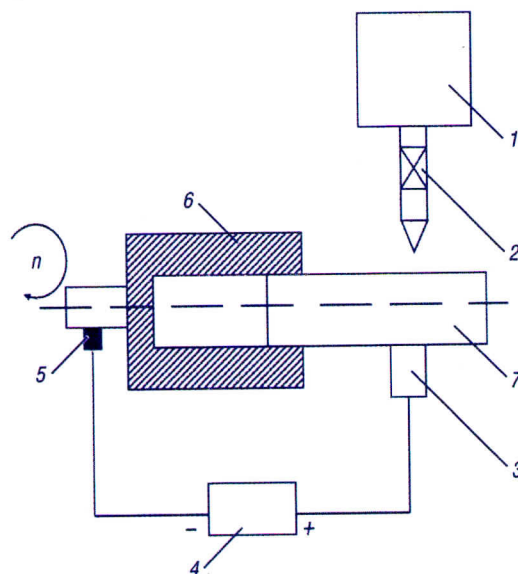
Схема электрохимико-механической обработки: 1 — емкость с ИОЖ; 2 — кран; 3 — инструмент-анод; 4 — источник тока; 5 — щетки; 6 — патрон; 7 — обрабатываемая деталь
